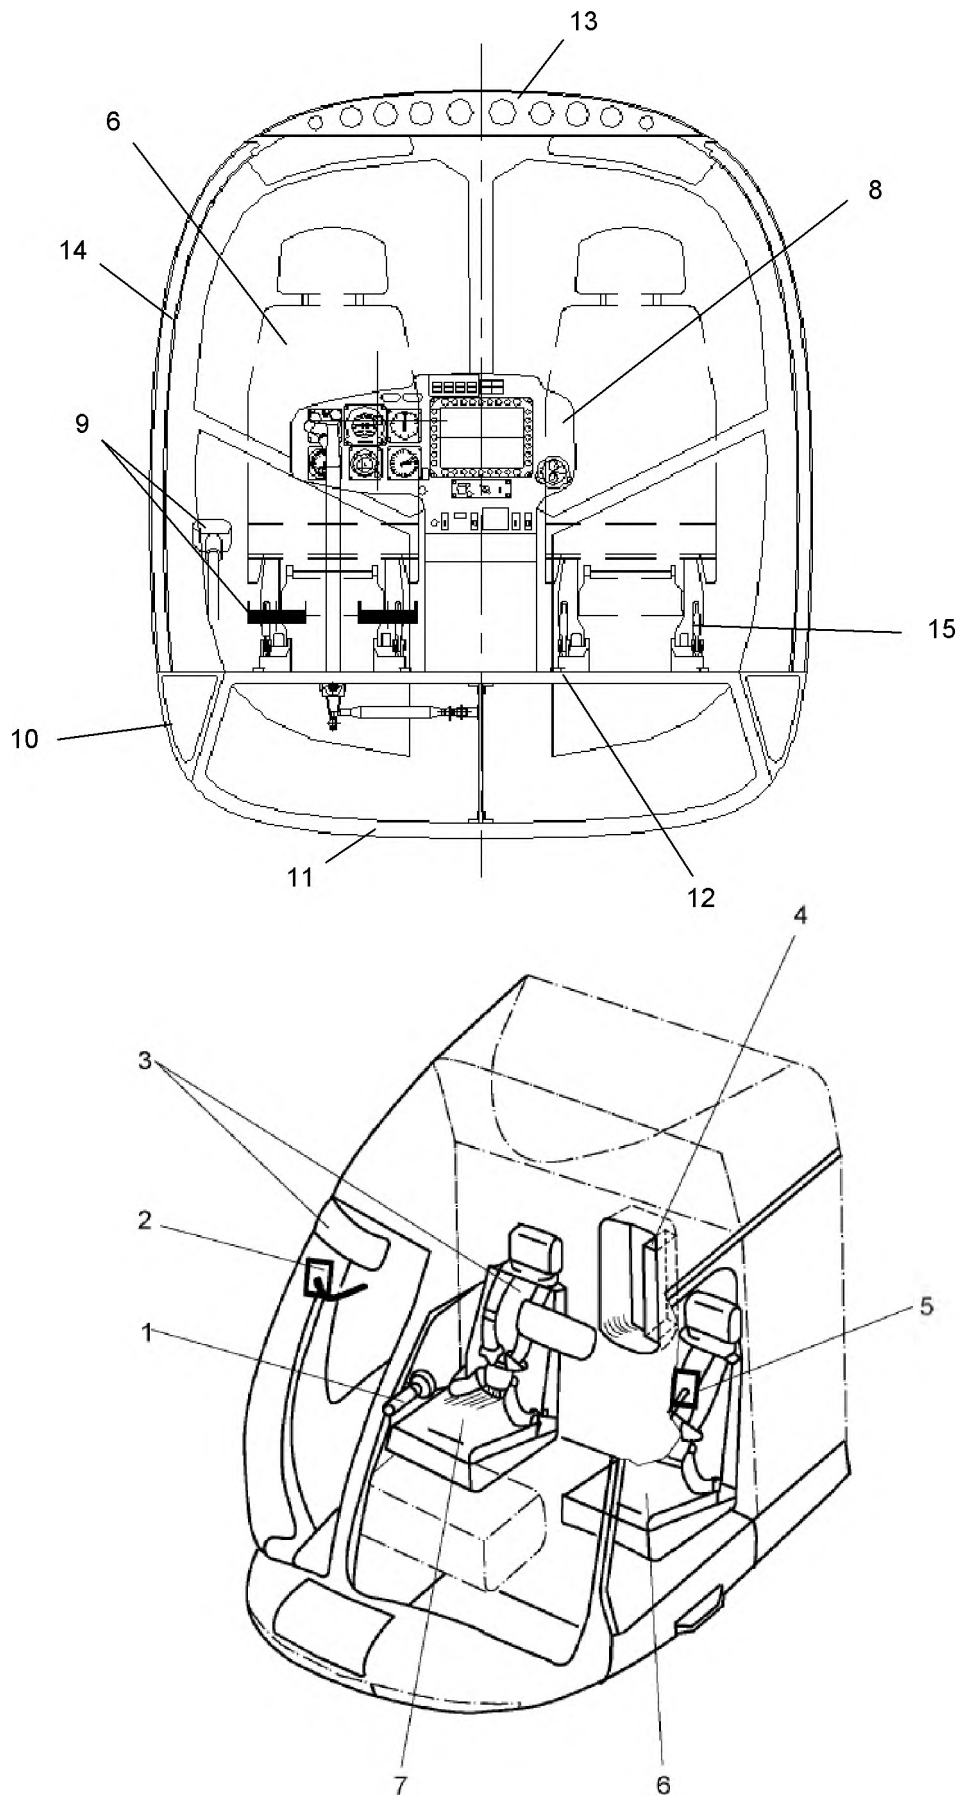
Конструкция кабины экипажа вертолета Ка-226 [12]:
